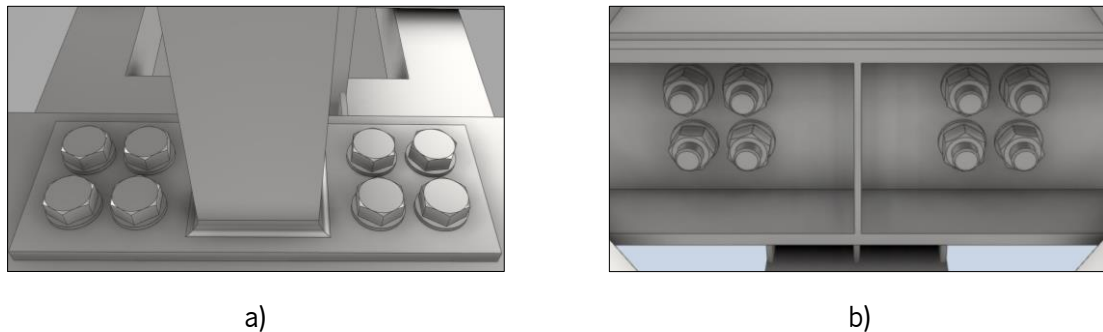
Ligação aparafusada do tubo de elevação à barra U estrutural vista de cima e vista de baixo, respetivamente em a) e b).
